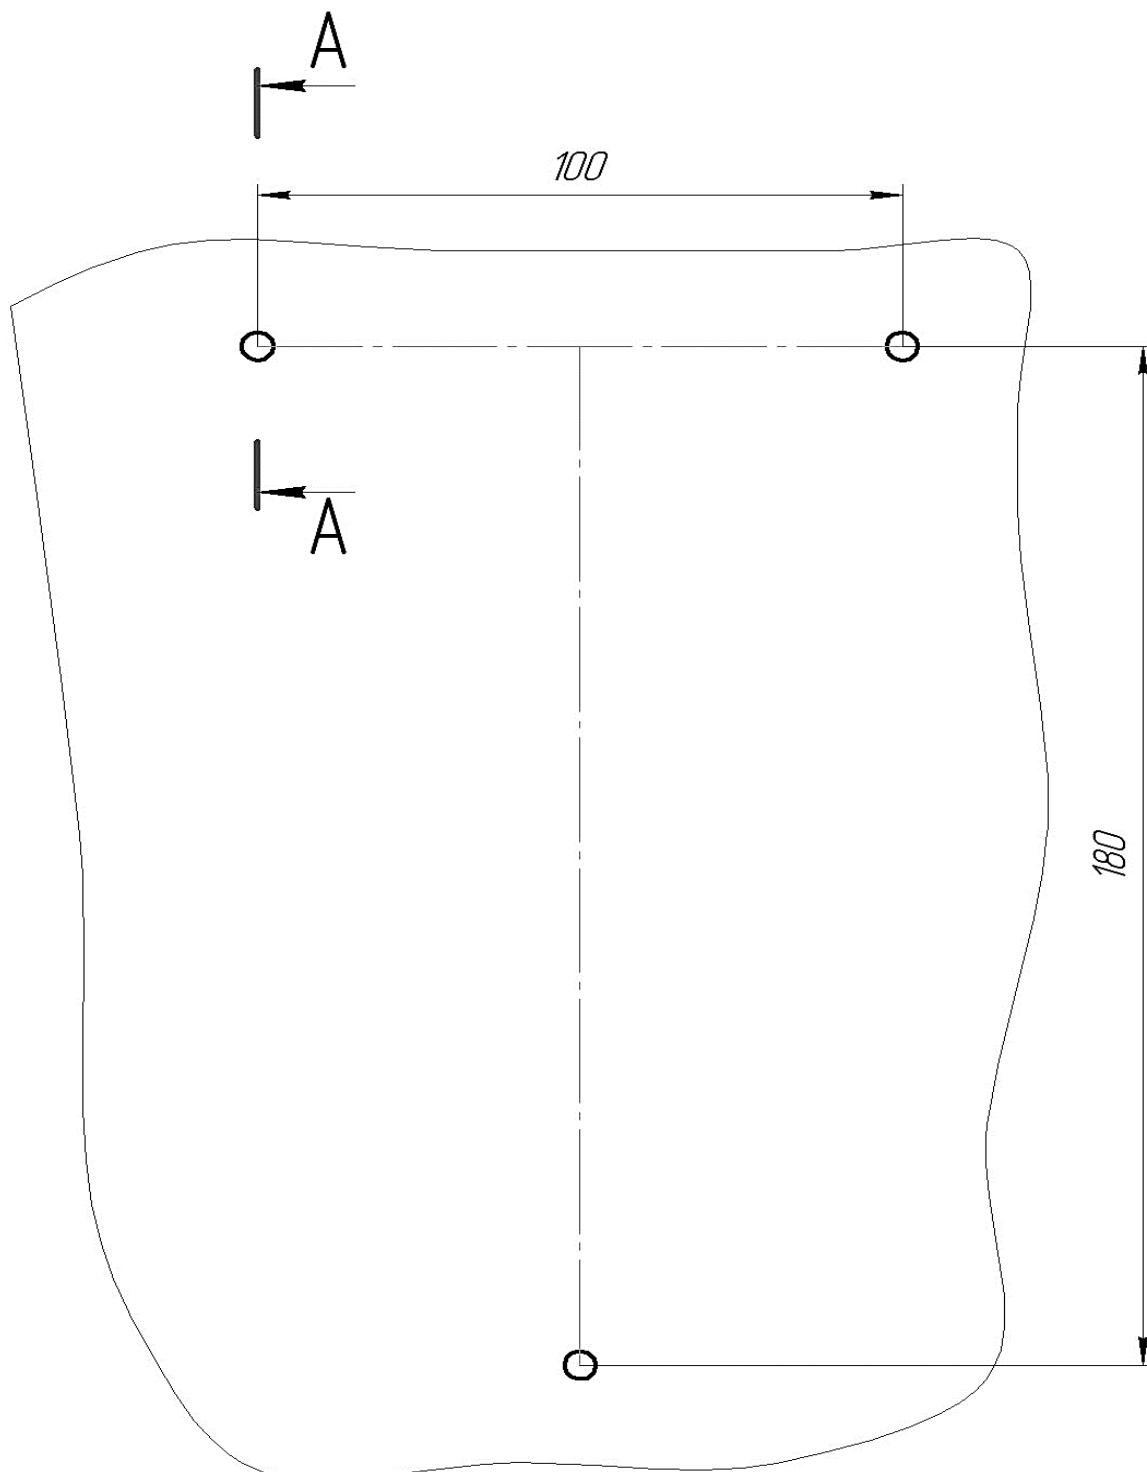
Разметка отверстий для крепления Блока ПУИ
